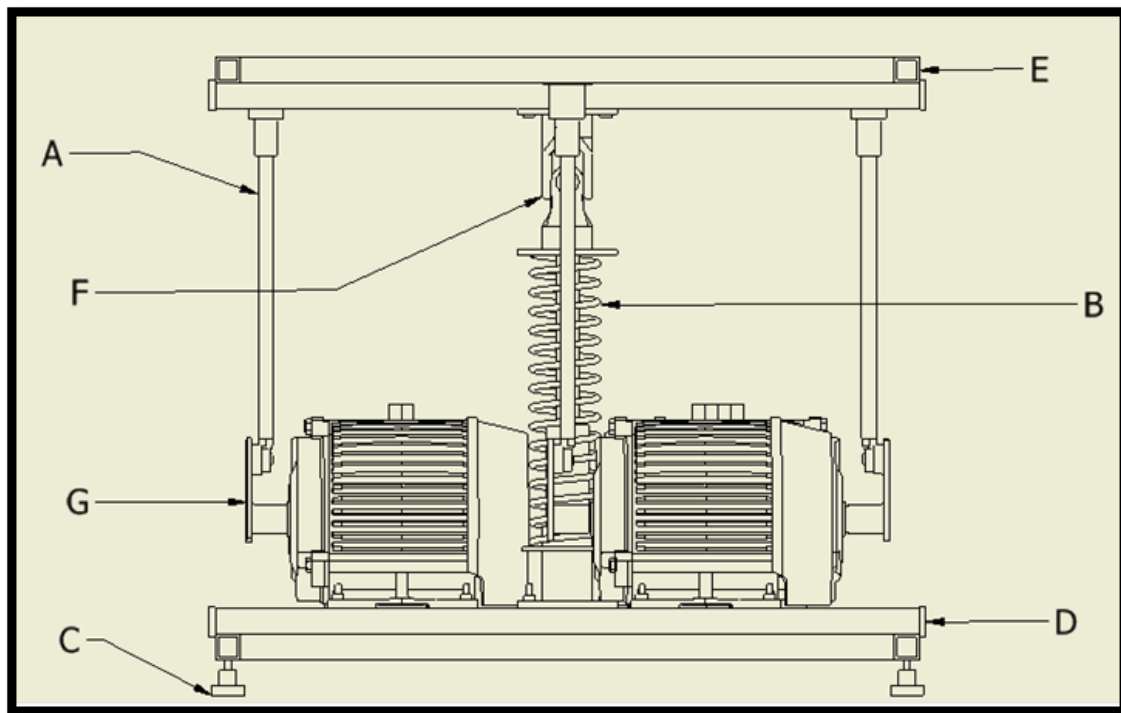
29 Vista frontal de ensamble de modulo generador de movimientos oscilatorios
